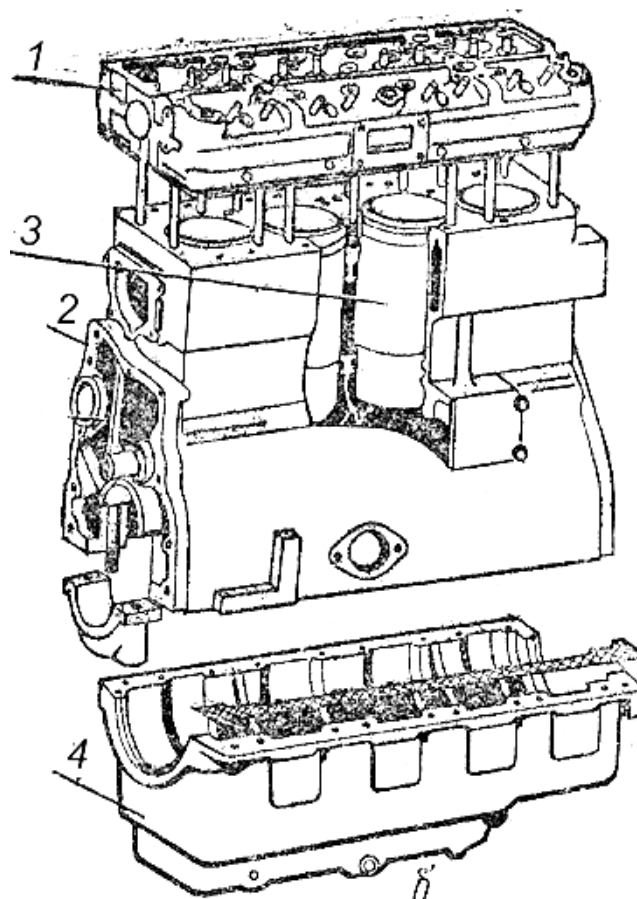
Основні корпусні деталі дизельного двигуна:
